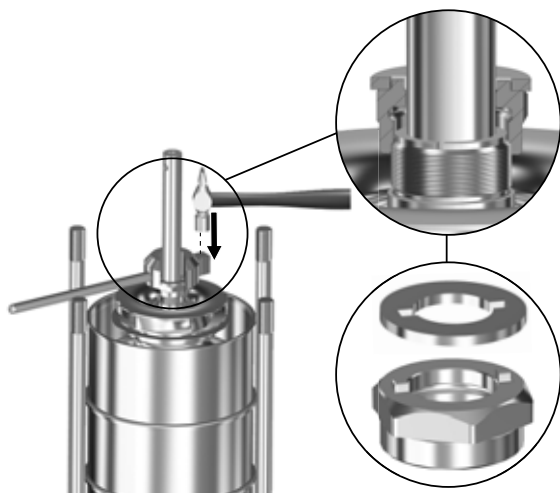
Снятие рабочего колеса (49 или 49а) с помощью приспособления Q
